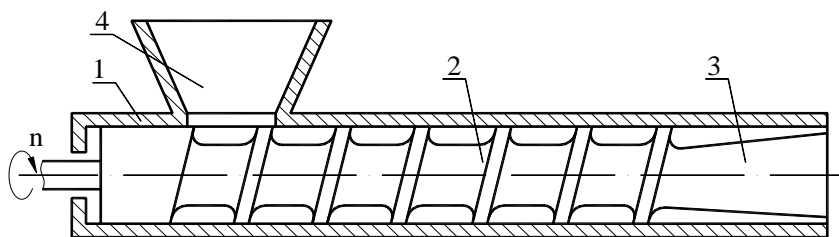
Екструдерний пристрій для переробки відходів:
